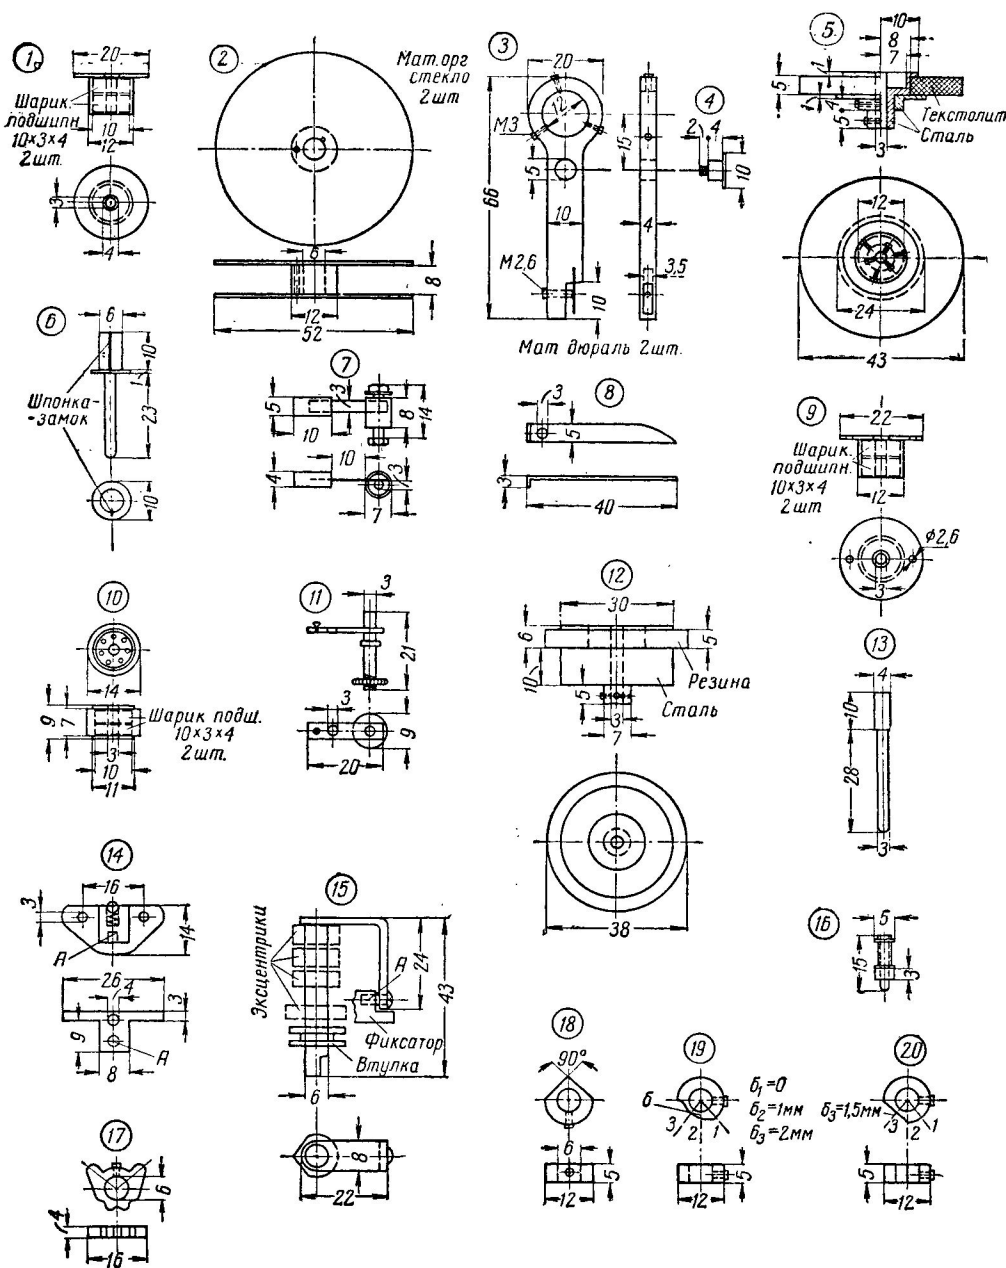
Детали лентопротяжного механизма: 1 — втулка кассеты, 2 — кассета, 3 — большой рычаг, 4 — винт крепления рычага, 5 — фрикционный механизм, 6 — ось кассеты, 7 — фетровый тормоз, 8 — малый рычаг, 9 — втулка ведущего ролика, 10 — прижимной ролик, 11 — ось с рычагом прижимного ролика, 12 — маховик, 13 — ведущий ролик, 14 — фиксатор, 15 — ось эксцентров, 16 — скользящий ролик, 17 — фасонный эксцентрик, 18 — эксцентрик двигателя, 19 — эксцентрик включения прямого и обратного хода двигателя, 20 — эксцентрик включения блока головок.
